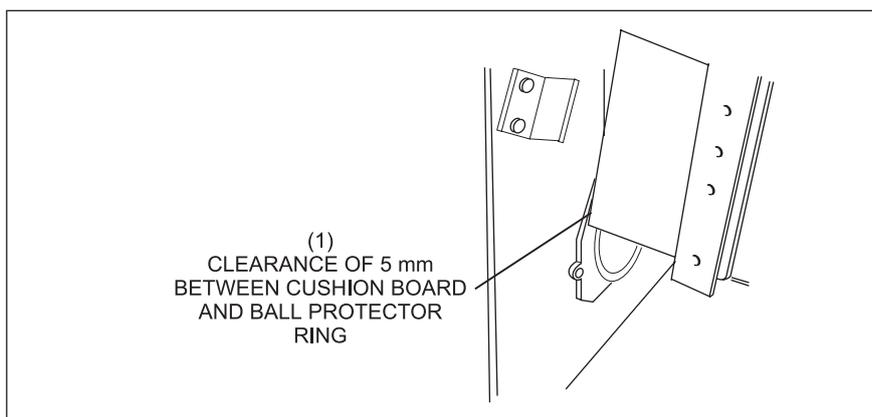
5 mm d'espace entre le panneau de coussinet et la bague de protection de boule.
